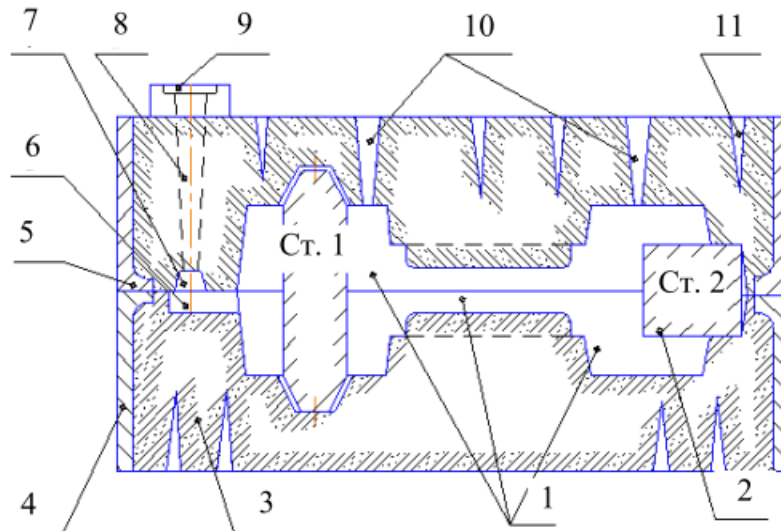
Литейная форма для получения отливки рычага: 1 – полость формы; 2 – стержни; 3 – формовочная смесь; 4 – нижняя опока; 5 – верхняя опока; 6 – питатель; 7 – шлакоуловитель; 8 – стояк; 9 – литниковая чаша; 10 – выпоры; 11 – газоканалы
